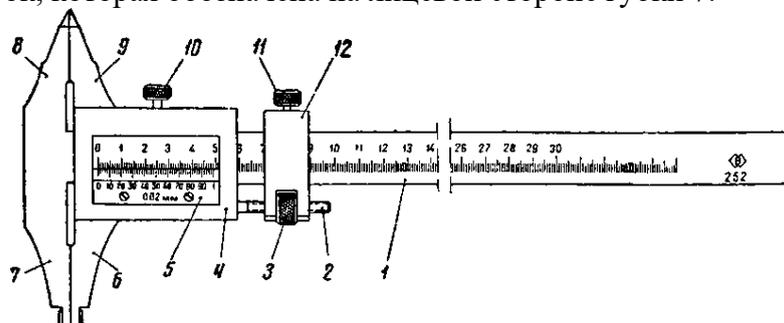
Конструкция штангенциркуля ШЦ-II: 1 – штанга; 2 – винт микрометрической подачи рамки; 3 – гайка микровинта; 4 – рамка; 5 – нониусная пластинка; 6 и 9 – подвижные губки; 7 и 8 – неподвижные губки; 10 и 11 – стопорные винты; 12 – хомут; Рамка 4 и хомут 12 соединены между собой микрометрическим винтом 2 с гайкой 3. При помощи этого устройства осуществляется малая подача рамки. Положение рамки и хомута фиксируется винтами.
